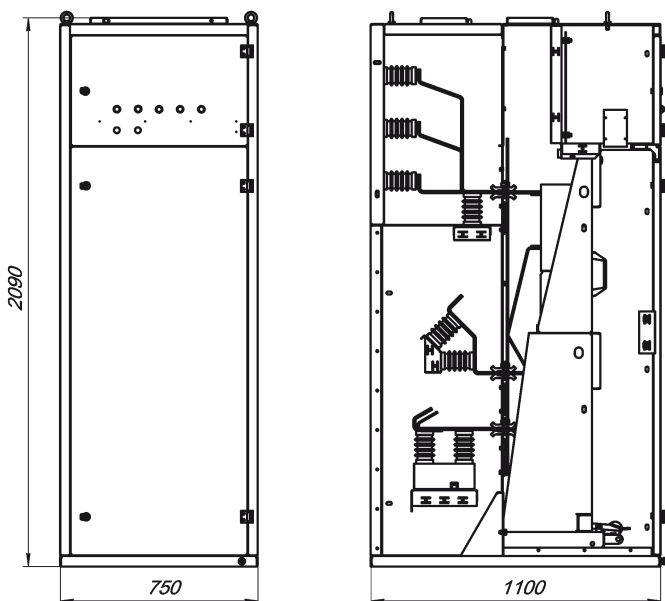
Габаритные размеры ШВК-10-4/320-2
